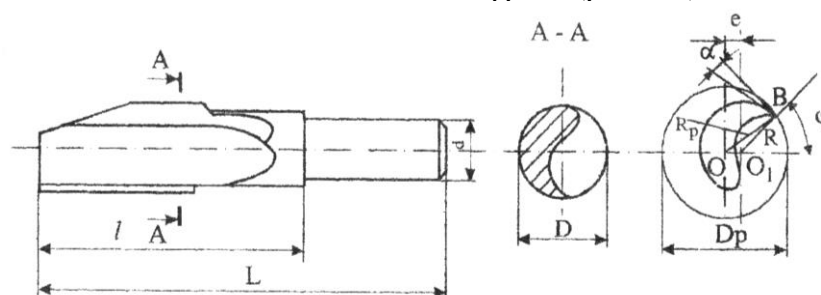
Конструкція однозубої незатілової фрези: а - фреза; б - схема установа фрези з ексцентриситетом
